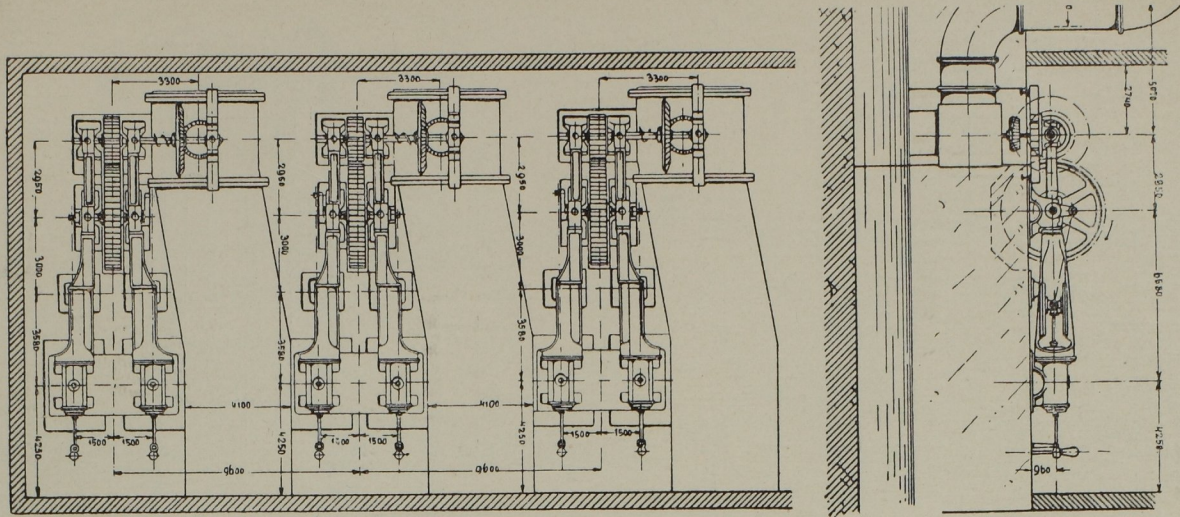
Kompressor-Anlage der Chapin-Mine in Iron Mountains, Michigan. Masst. 1:275.
